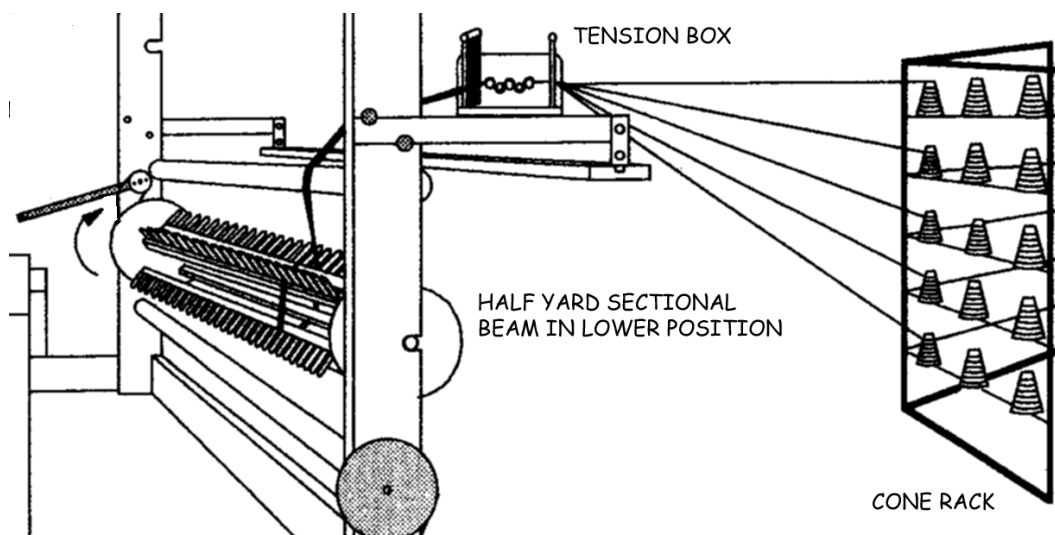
Déformation du faisceau sectionnel Half Yard en position basse
